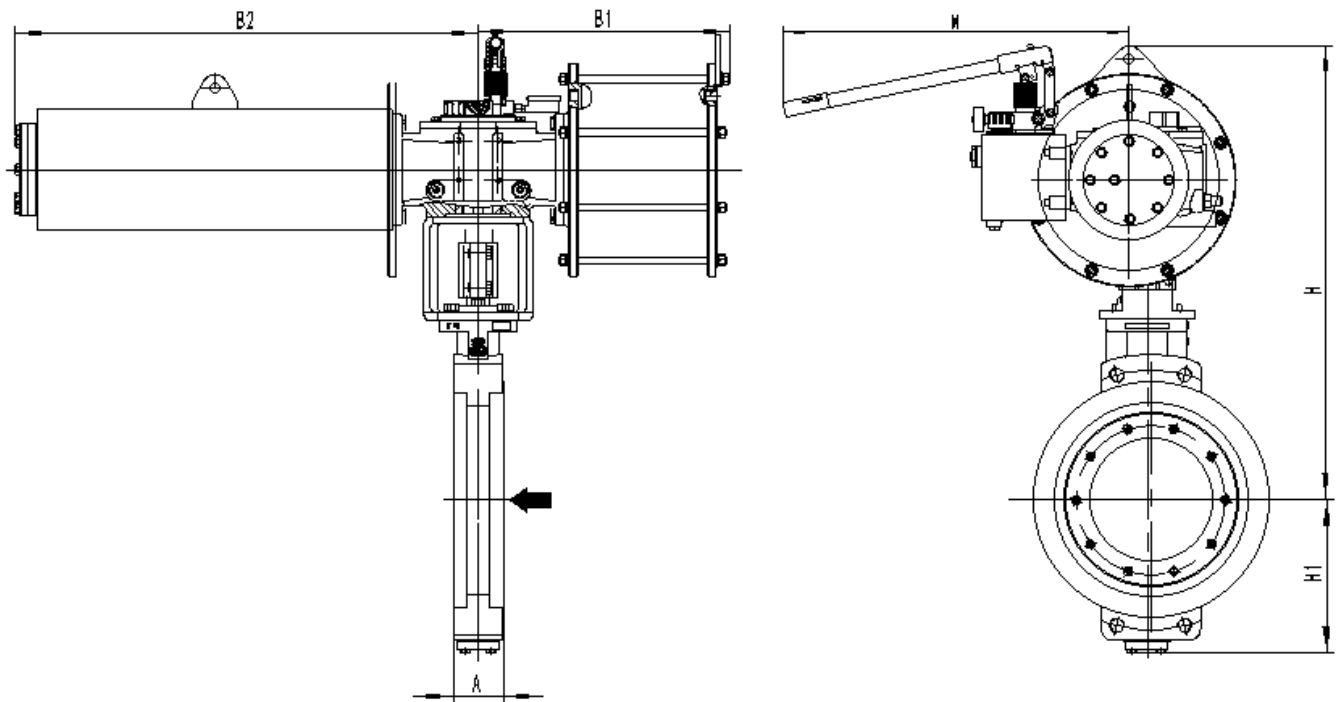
配 AW45SD43~AW85SD56 带液压手轮外形尺寸图(FO 此状态为执行机构通气状态)
